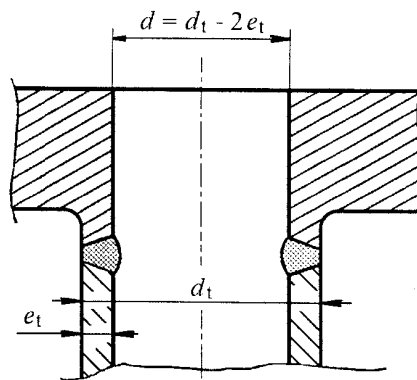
Tubo soldado a tope a la cara interior de la placa de tubos con cubo
